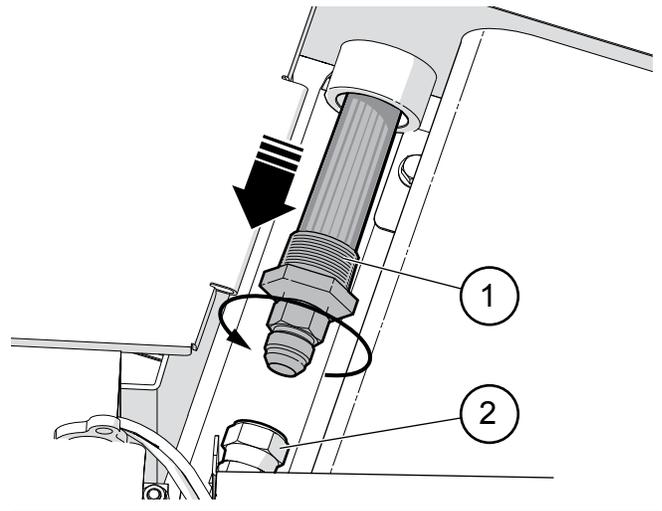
Crépine d'aspiration à l'arrière du réservoir d'huile hydraulique
